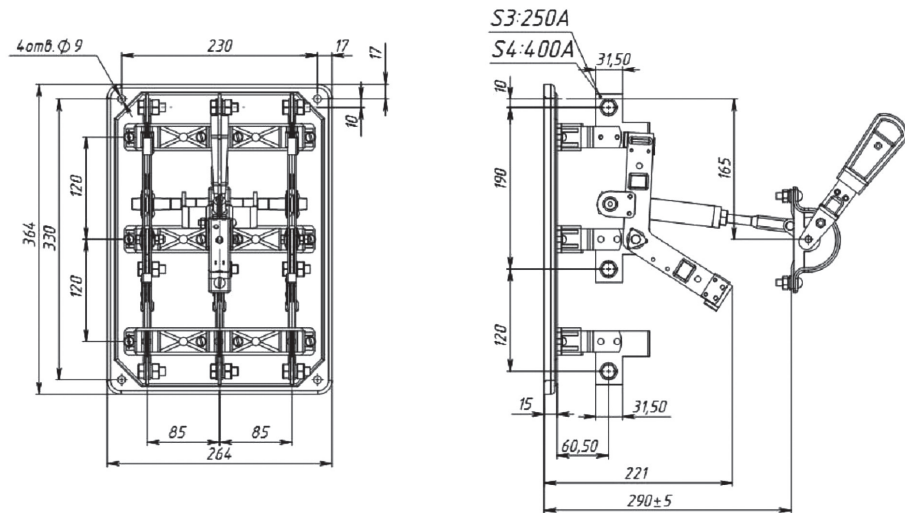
Б. Разъединитель типа П с центральным приводом на токи 250 А и 400 А
